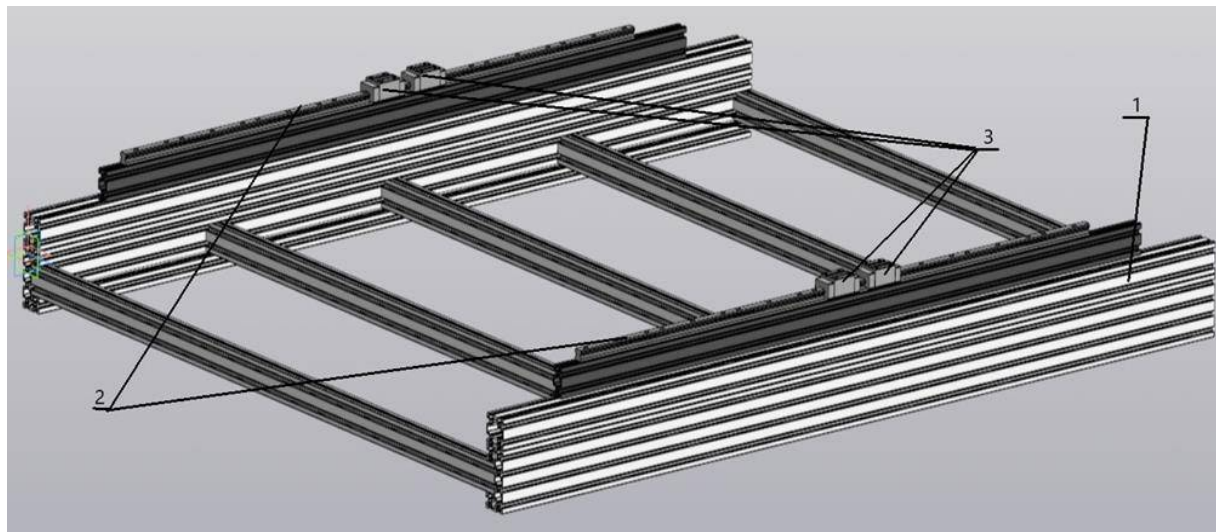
Общий вид станины с направляющими 3D принтера ОТМ М:
